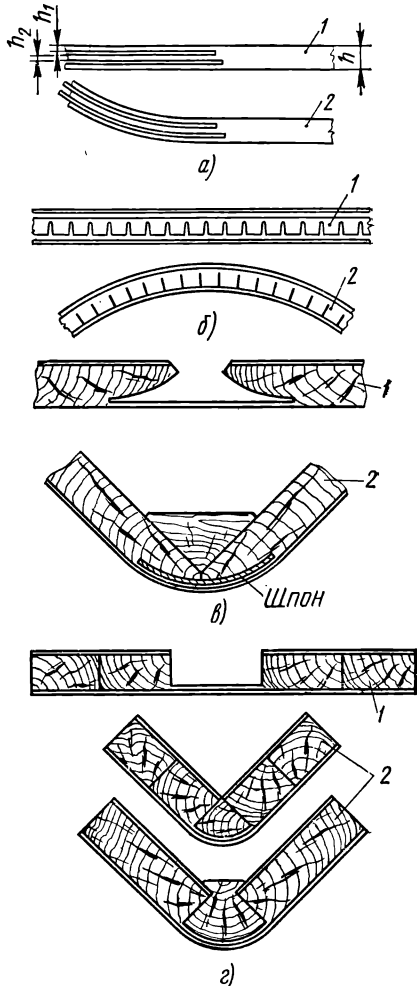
Гнутопропильные детали: а — с продольными пропилами на концах деталей, б — с пропилами в плитах, в, г — с пазами в плитах; 1 — заготовки до склеивания, 2 — заготовки после склеивания
